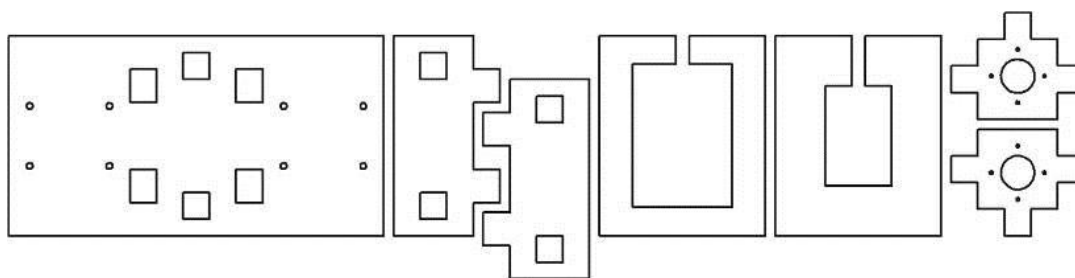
Ескізне креслення несучого корпусу каретки приводу
